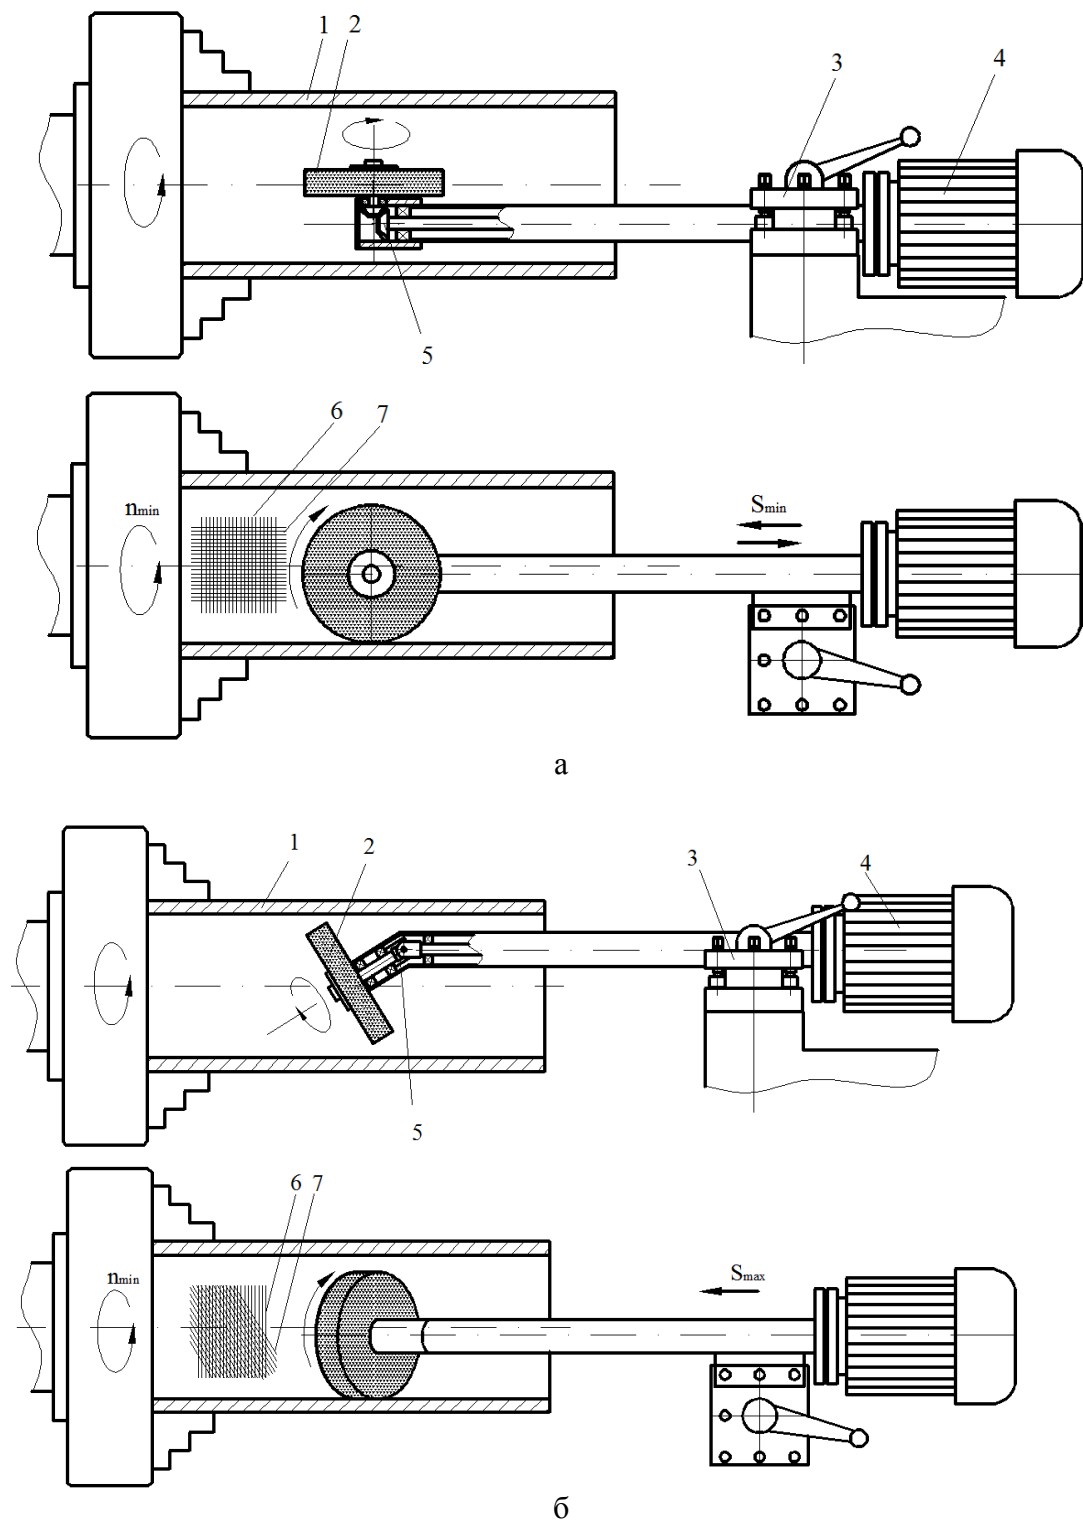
Схемы финишной обработки отверстия цилиндра:
